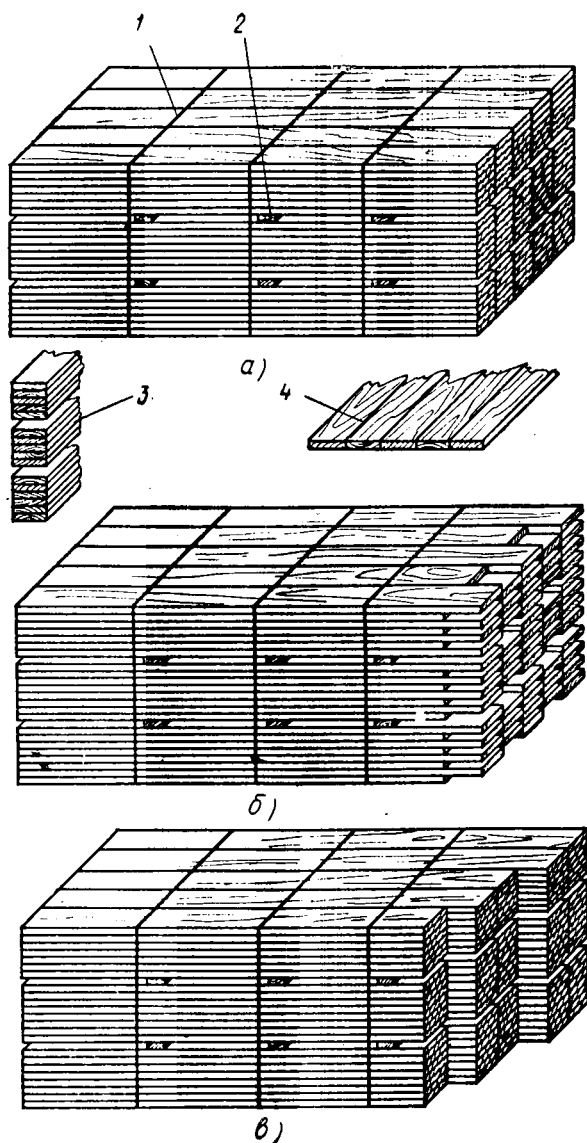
Конструкции транспортных пакетов пиломатериалов:
